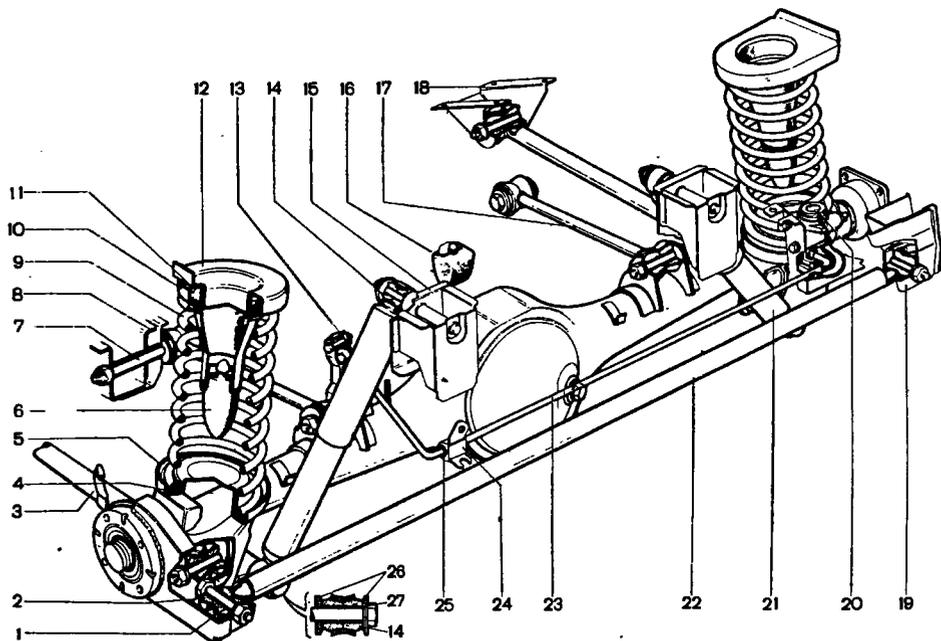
Задняя подвеска: 1 - распорная втулка; 2 - резиновая втулка; 3 - нижняя продольная штанга; 4 - нижняя изолирующая прокладка пружины; 5 - нижняя опорная чашка пружины; 6 - буфер хода сжатия подвески; 7 - болт крепления верхней продольной штанги; 8 - кронштейн крепления верхней продольной штанги; 9 - пружина подвески; 10 - верхняя чашка пружины; 11 - верхняя изолирующая прокладка пружины; 12 - опорная чашка пружины; 13 - тяга рычага привода регулятора давления задних тормозов; 14 - резиновая втулка проушины амортизатора; 15 - кронштейн крепления амортизатора; 16 - дополнительный буфер хода сжатия подвески; 17 - верхняя продольная штанга; 18 - кронштейн крепления нижней продольной штанги; 19 - кронштейн крепления поперечной штанги к кузову; 20 - регулятор давления задних тормозов; 21 - амортизатор; 22 - поперечная штанга; 23 - рычаг привода регулятора давления; 24 - обойма опорной втулки рычага; 25 - опорная втулка рычага; 26 - шайбы; 27 - дистанционная втулка
